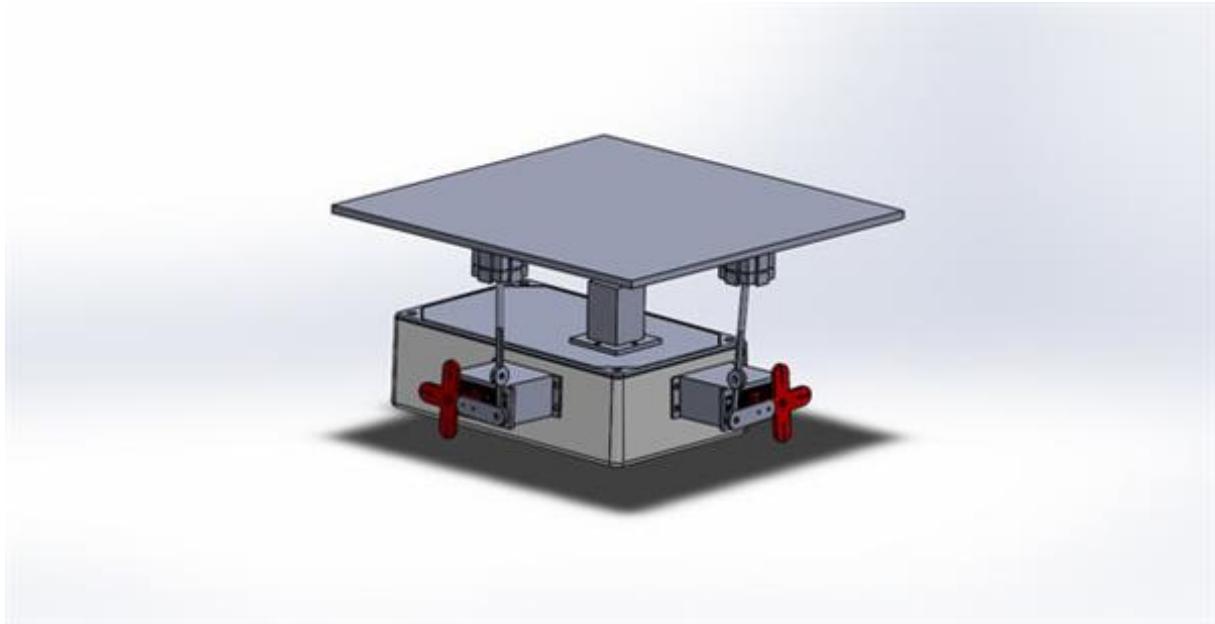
Ball on a Plate CAD [Ben15]
